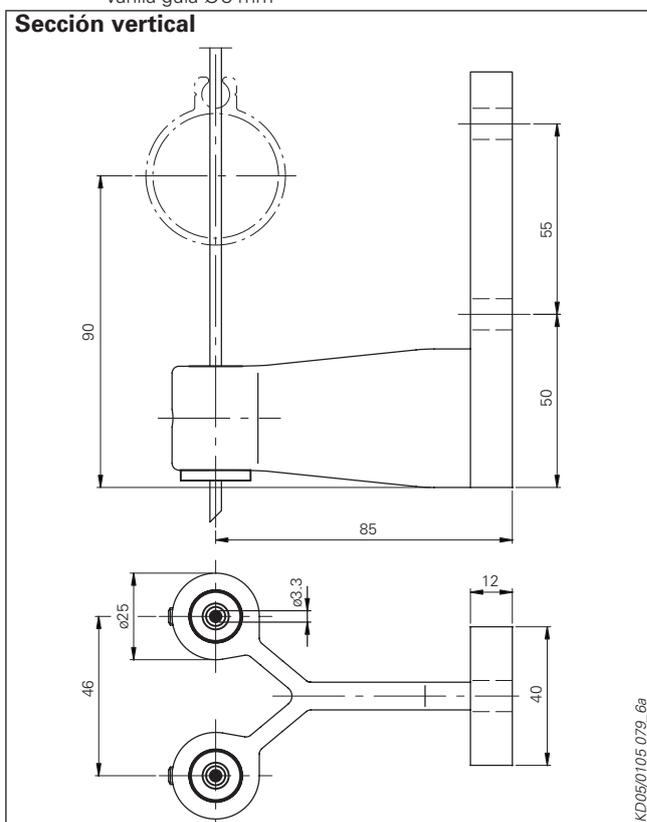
Sección vertical toldo para fachadas Modelo 207, portavara para instalación en grupo (en fundición de aluminio) para cable de guía Ø3,3 mm
